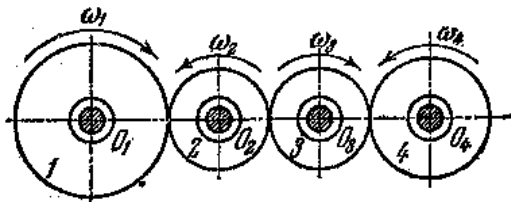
Схема рядового соединения зубчатых колес с паразитными колесами
